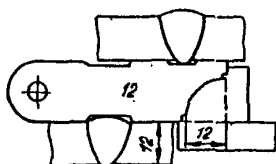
Специальный шаблон для контроля сварных швов
